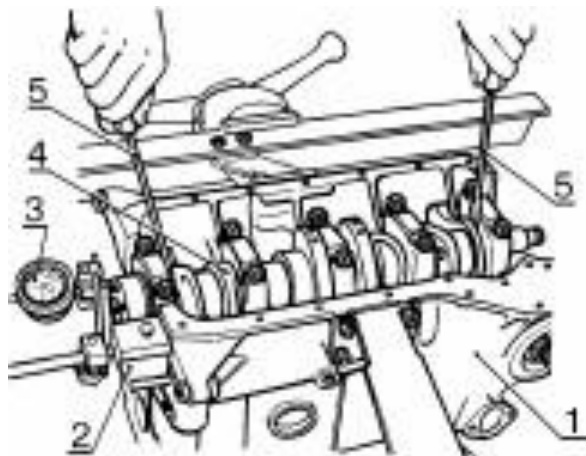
Схема перевірки осьового зазору колінвала.
